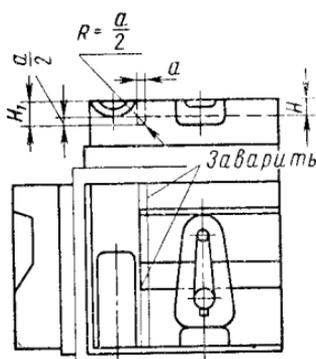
Замок, изготовленный строжкой до канавки для выхода резца
